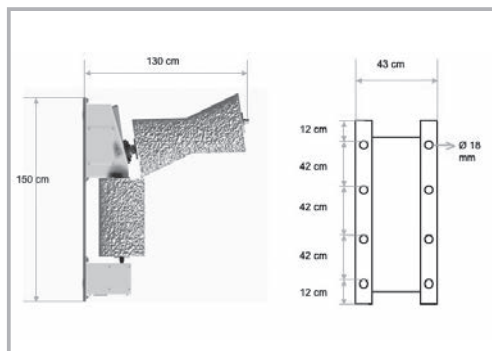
RotaBrush Twin: assieme e particolare piastra fissaggio a parete
